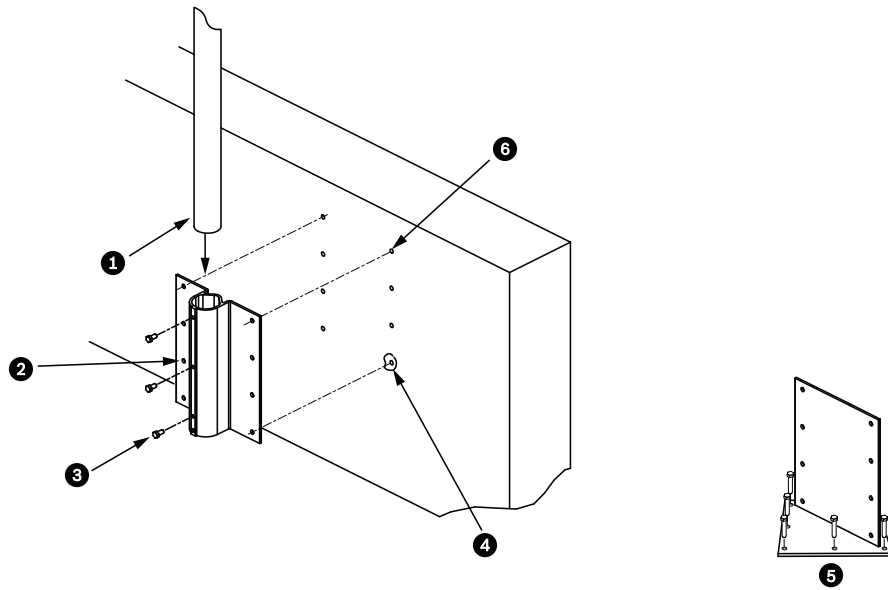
Soporte de sujeción en pared y placa de montaje en azotea
